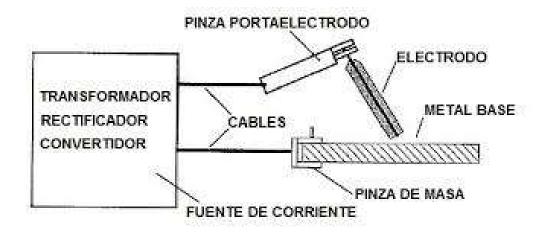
Esquema de funcionamiento de soldadura por electrodo (ingemecánica)
